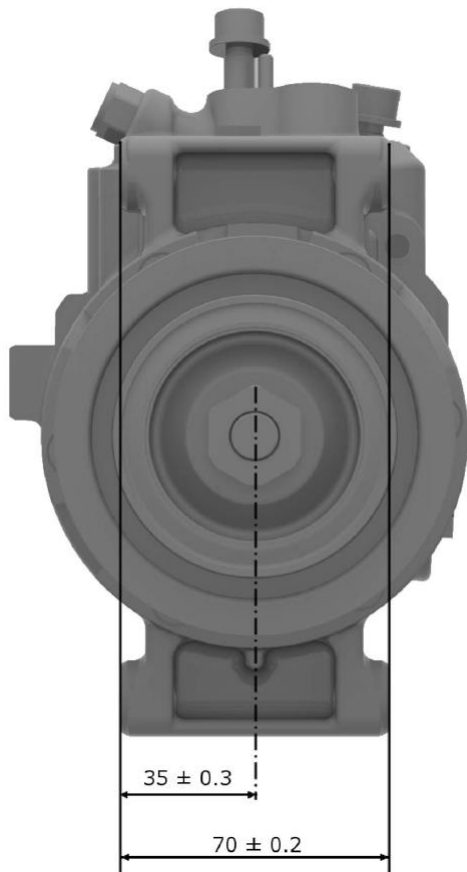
Размеры компрессора климатической установки Denso 6SU14 (вид спереди)
